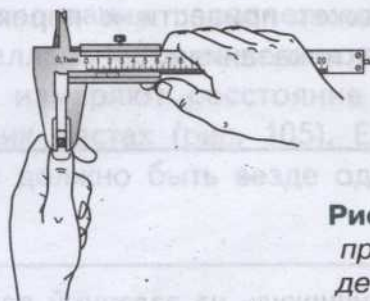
Положение рук при измерении размера детали штангенциркулем
